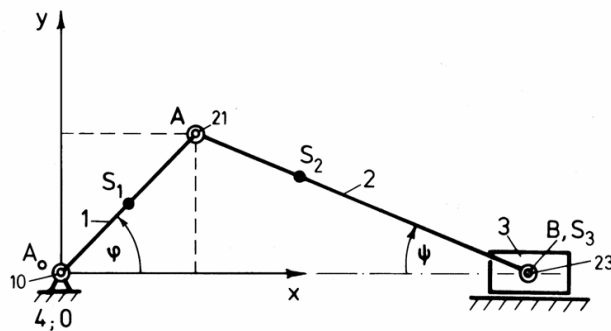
Diskretes Modell einer Einzylinder-Hubkolbenmaschine
